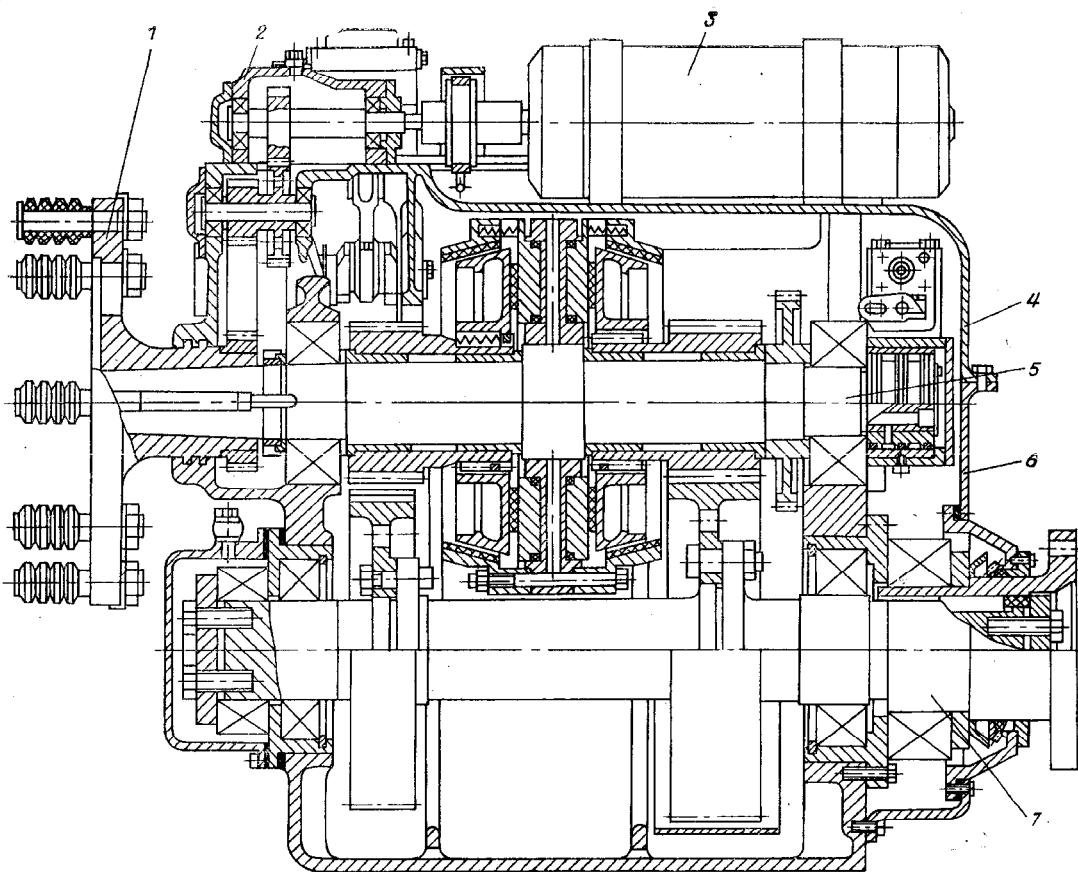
Реверсивно-редукторная передача 27РРП-230. Продольный разрез:
